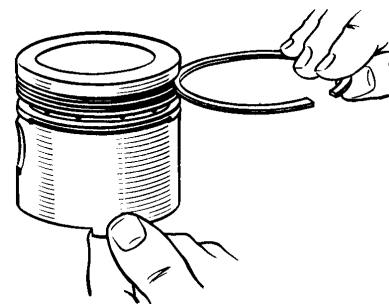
Проверка свободного перемещения поршневого кольца в канавке поршня. При установке поршневых колец на поршни устанавливают радиальный расширитель 5 (см. рис. 7), нижний диск 3, осевой расширитель 4 и верхний диск, затем устанавливают нижнее и верхнее компрессионные кольца. При установке компрессионных колец прямоугольная фаска, выполненная на внутренней поверхности, должна быть обращена вверх. После установки колец нужно смазать поршни и поршневые кольца маслом и еще раз проверить легкость перемещения колец в канавках и расставить стыки колец, как показано на рис. 7.
